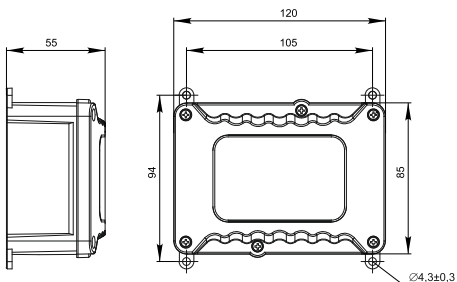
Габаритные размеры коробки WTP-408 / Figure 7 – Overall dimensions of the WTP-408 box
